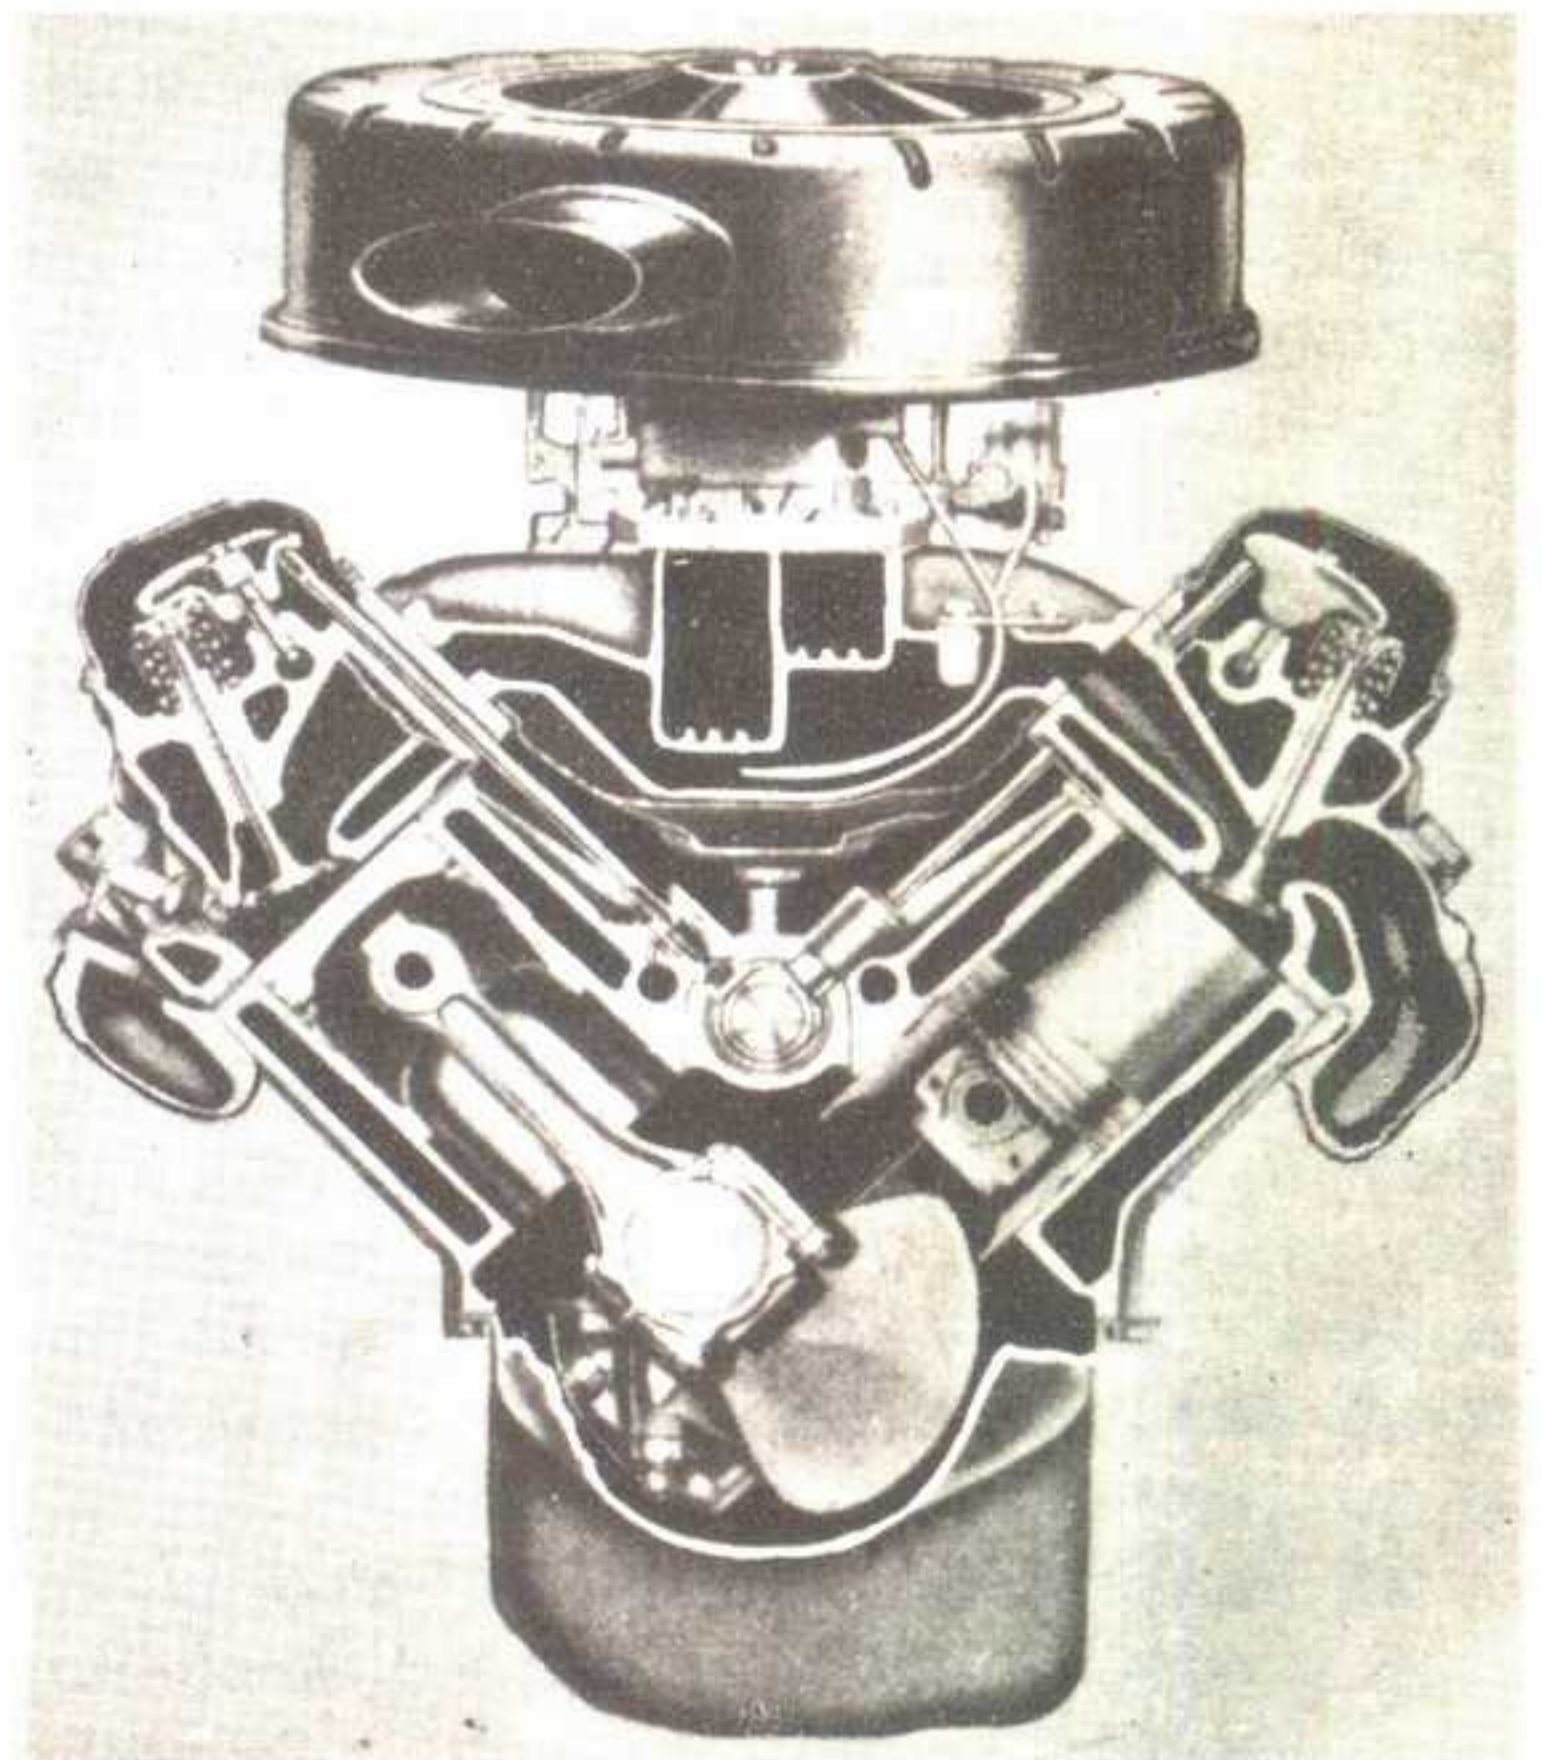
Corte de un motor de automóvil, 8 cilindros en V.
